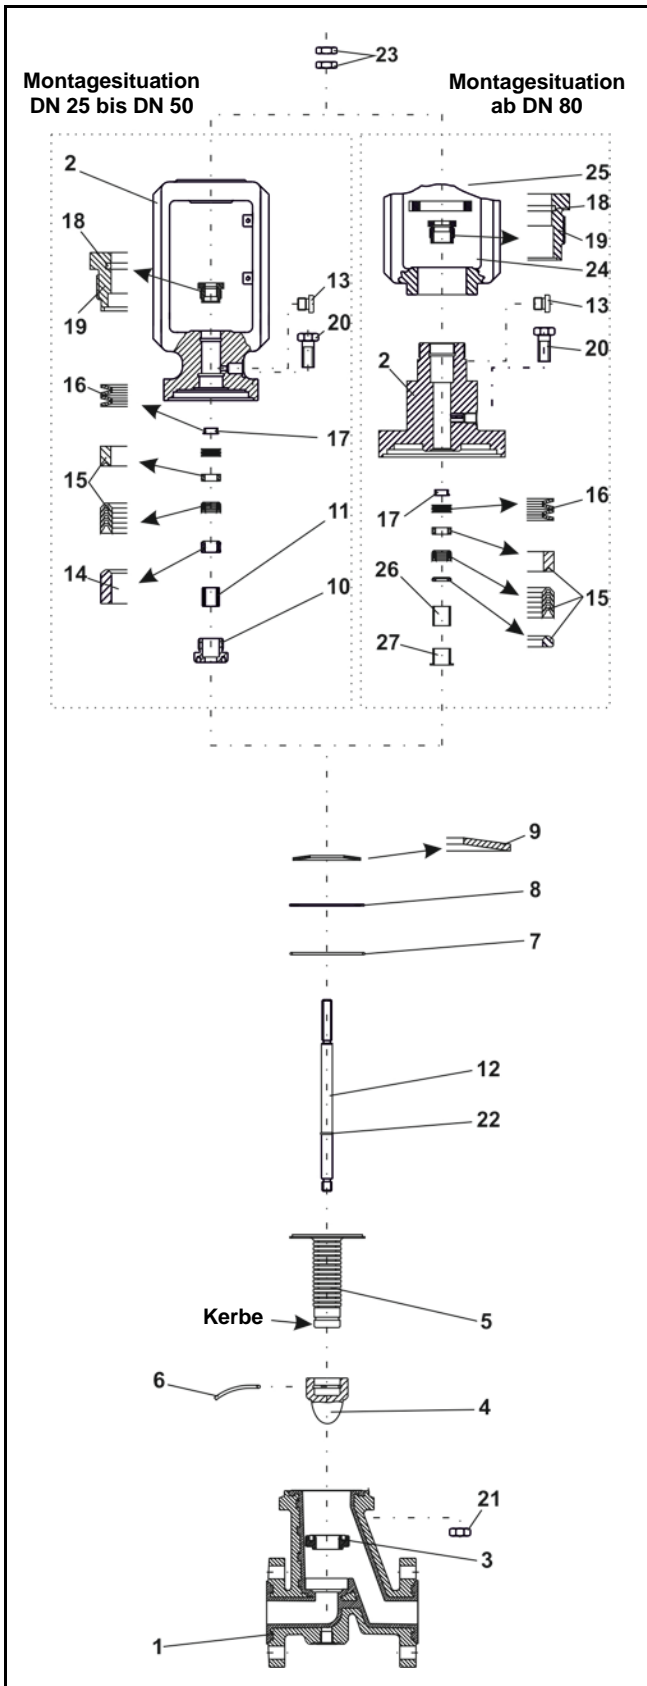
Explosionszeichnung des Stellventils BR 01b, bis Baujahr 2006
